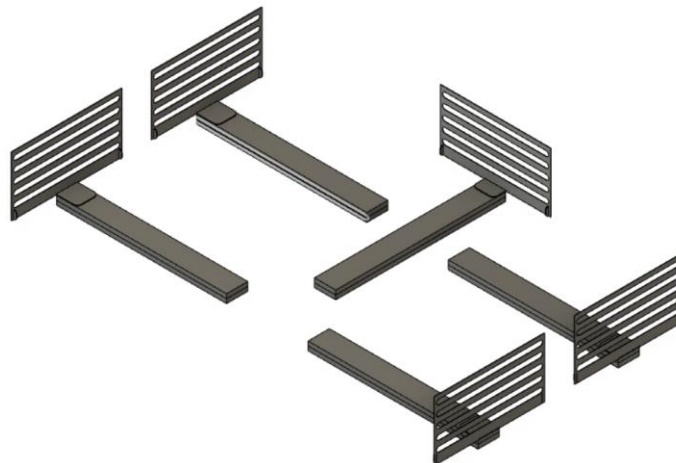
Diseño 3D Preliminar – Placas bimetálicas y rejillas de la barbacoa portátil (2020)
